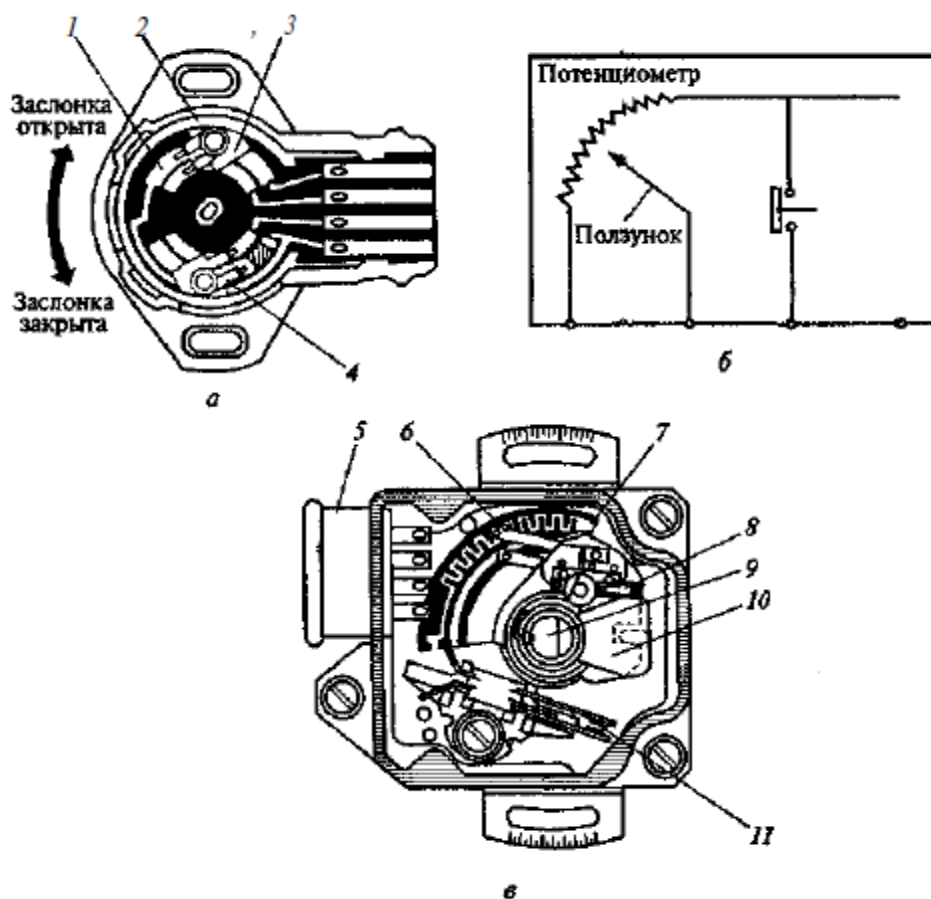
Датчики угла поворота дроссельной заслонки: а – реостатный; б – потенциометрический; в – дискретный; 1 – резистивный элемент; 2 – корпус; 3, 4 и 6 – ползунки; 5 – кабельный разъем; 7 – контактная пластина; 8 и 11 – контактные группы; 9 – привод; 10 – кулачок
